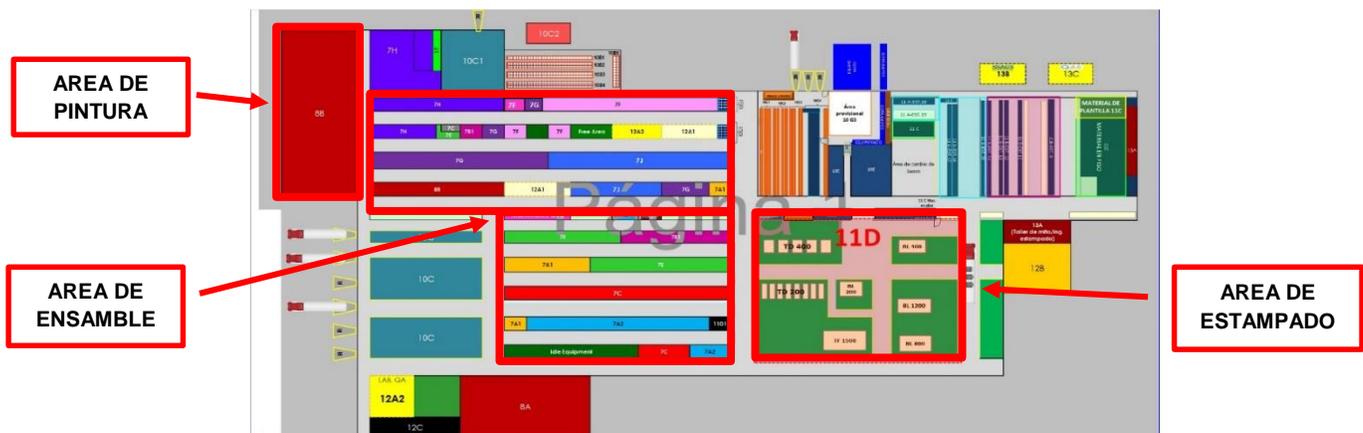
LAY OUT de Planta YOROZU MEXICANA. Fuente: YMEX 2023.
